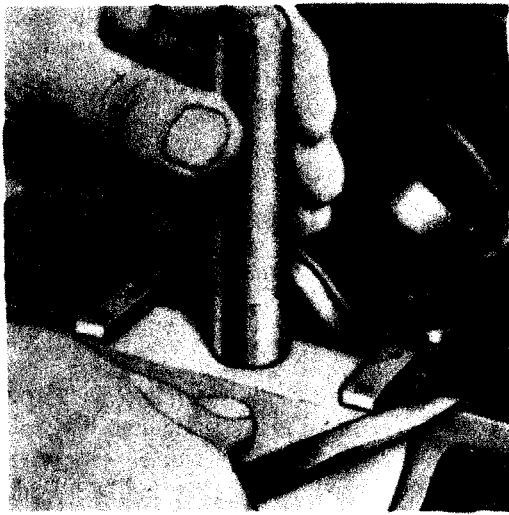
Instalación en el bloque motor de un cierre de estanqueidad de aceite en un cojinete de cigüeñal posterior por medio de una herramienta especial (Ford Motor Company).
